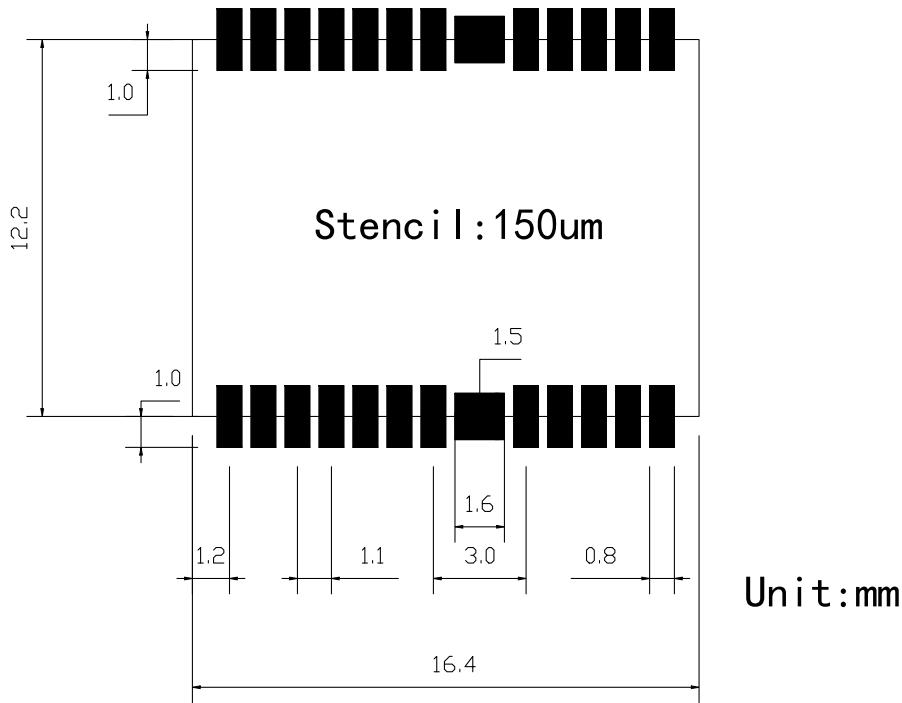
参考封装尺寸/Figure 11-2 Reference package dimensions
